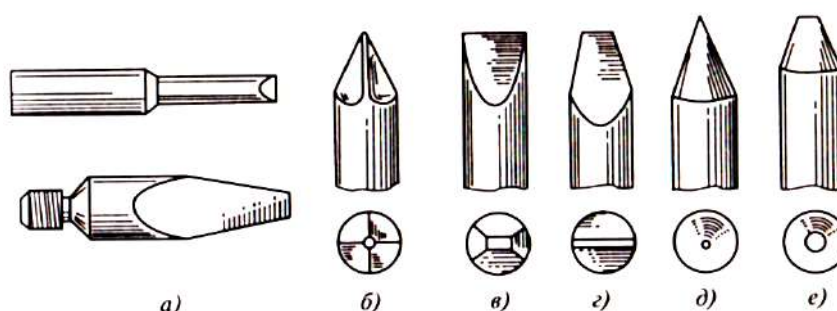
Виды сварочных наконечников (а) и формы заточки их рабочей части: б-пирамида; в-четырехгранный клин; г-клин; д-конус; е-усеченный конус
